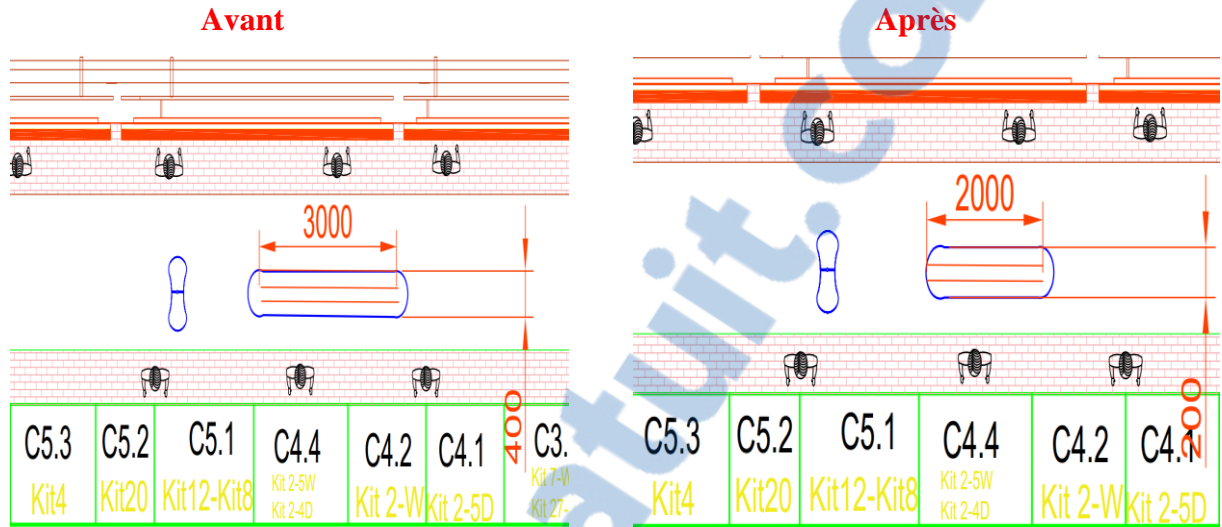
Ajustement des moyens de connexion de la zone Floor line1/line2
